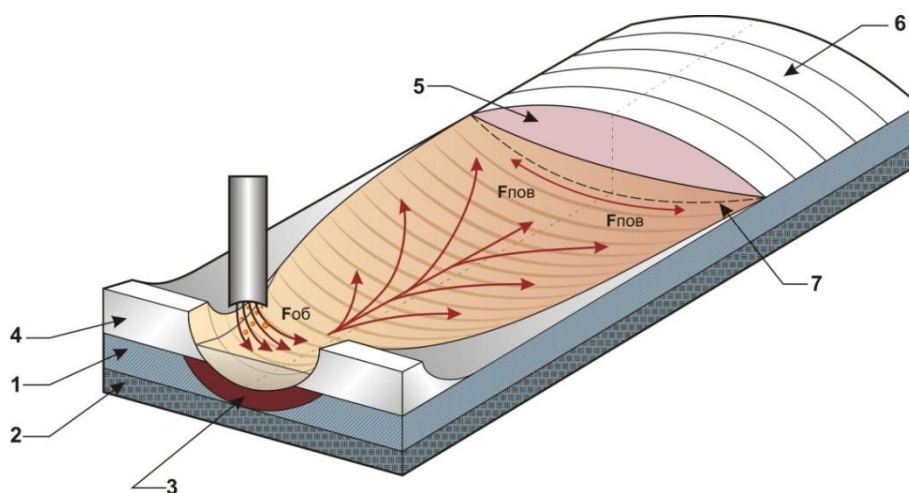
Модель образования обратного валика при односторонней сварке на подкладке: 1 – формирующий слой; 2 – тугоплавкий слой; 3 – шлаковая ванна; 4 – основной металл; 5 – хвостовая часть ванны; 6 – шов; 7 – граница формы обратного валика; $F_{пов}$ – силы межфазного натяжения на границе шлак-металл; $F_{об}$ – равнодействующая всех сил, действующих со стороны дуги и способствующих перемещению металла [Model of the formation of the return roller with one-sided welding on the lining: 1 – forming layer; 2 – refractory layer; 3 – slag bath; 4 – base metal; 5 – the tail portion of bath; 6 – the seam; 7 – reverse roller form border; $F_{пов}$ – interfacial tension forces at the slag-metal interface; $F_{об}$ – resultant of all forces acting from the side of the arc and promoting the movement of the metal]
